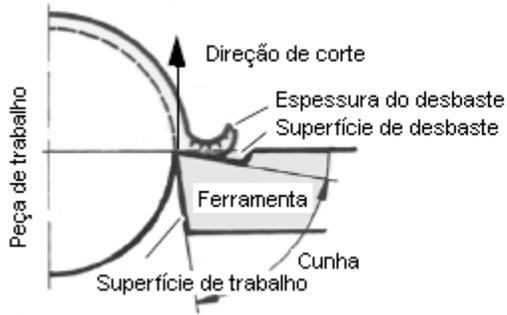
Fresa determinada geometricamente para o processo de separação
